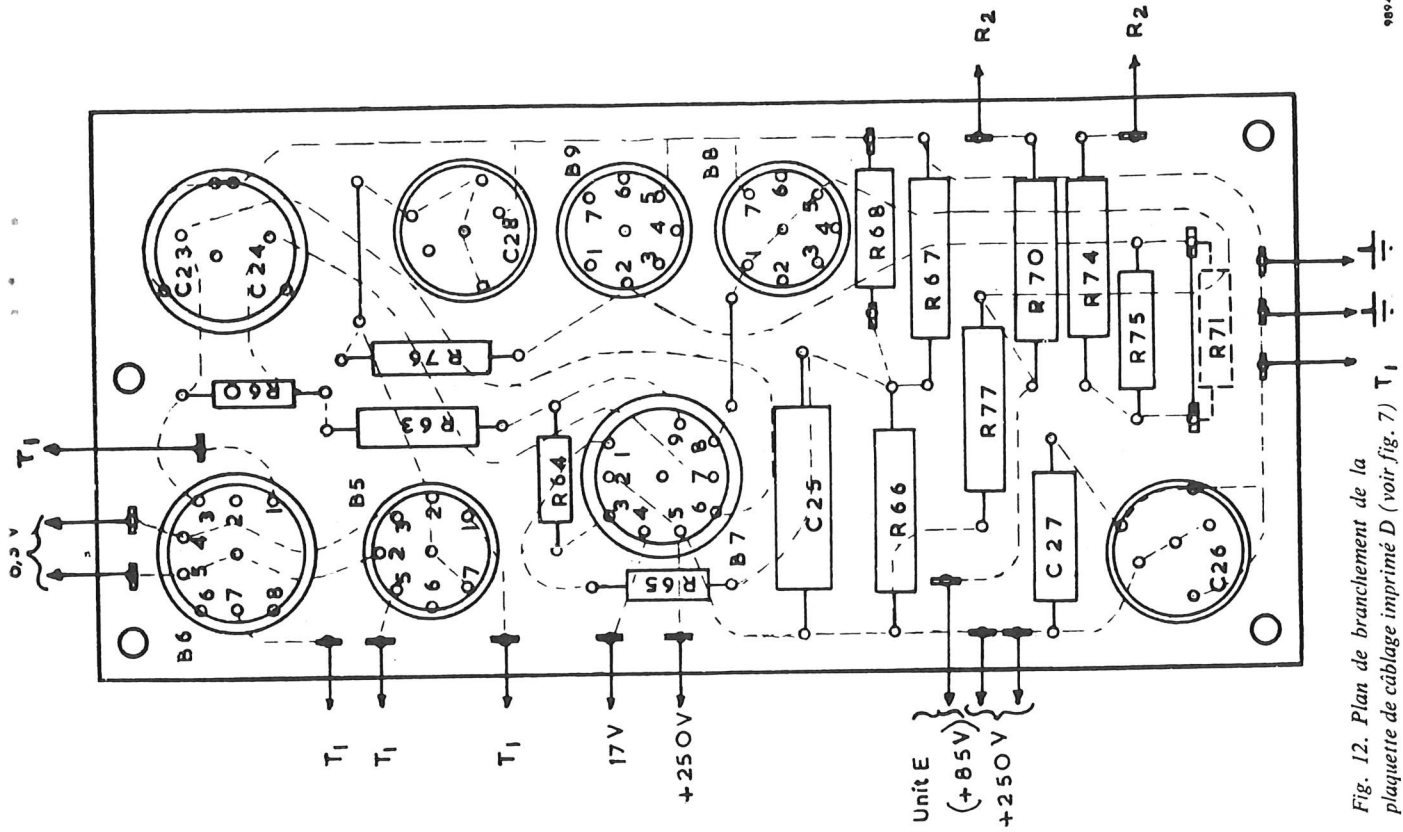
Plan de branchement de la plaque de câblage imprimé D (voir fig. 7) T₁
